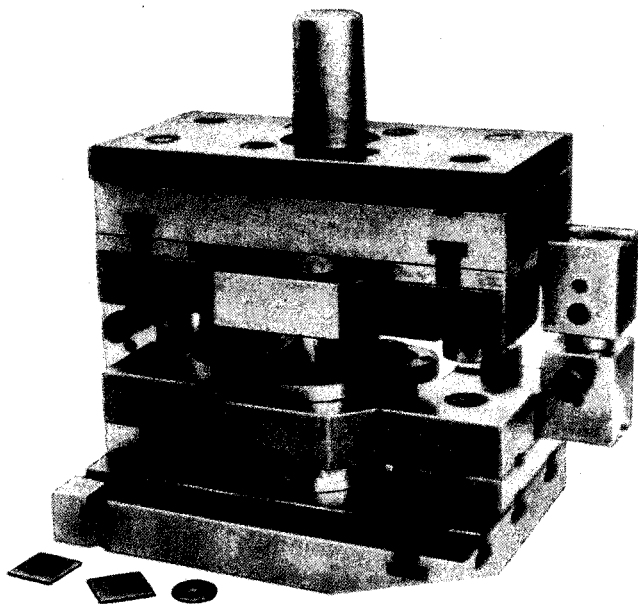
Штамп для холодной вырубке шайб из заготовок листовой стали
